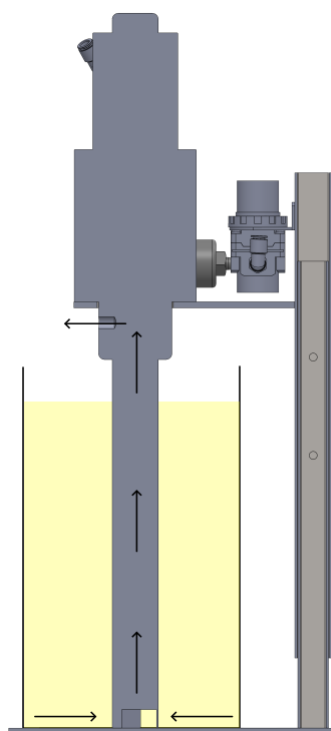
Pumpe PP-5 ohne Druckplatte
